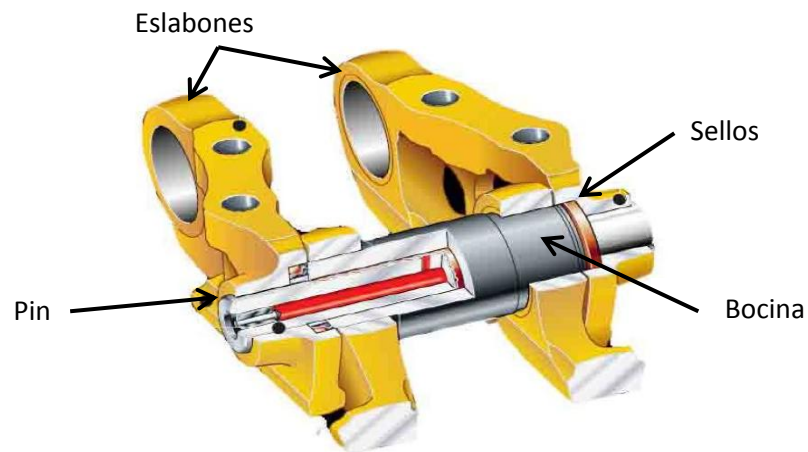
Partes de una cadena de carrilería en un tren de rodamiento lubricada.
